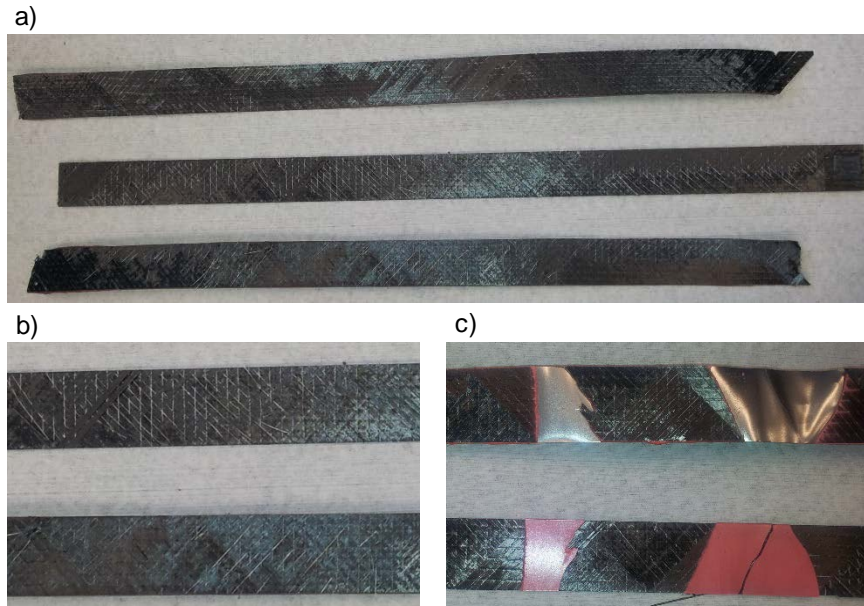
a) Bruchbild Stahl-CFK-Stahl Klebverbindung mit b) Delamination im CFK sowie c) teilweise adhäsivem Versagen zum Stahl (unten rechts)
